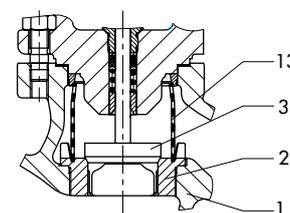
· Divisor de flujo St I, montado en válvula Tipo 3241
